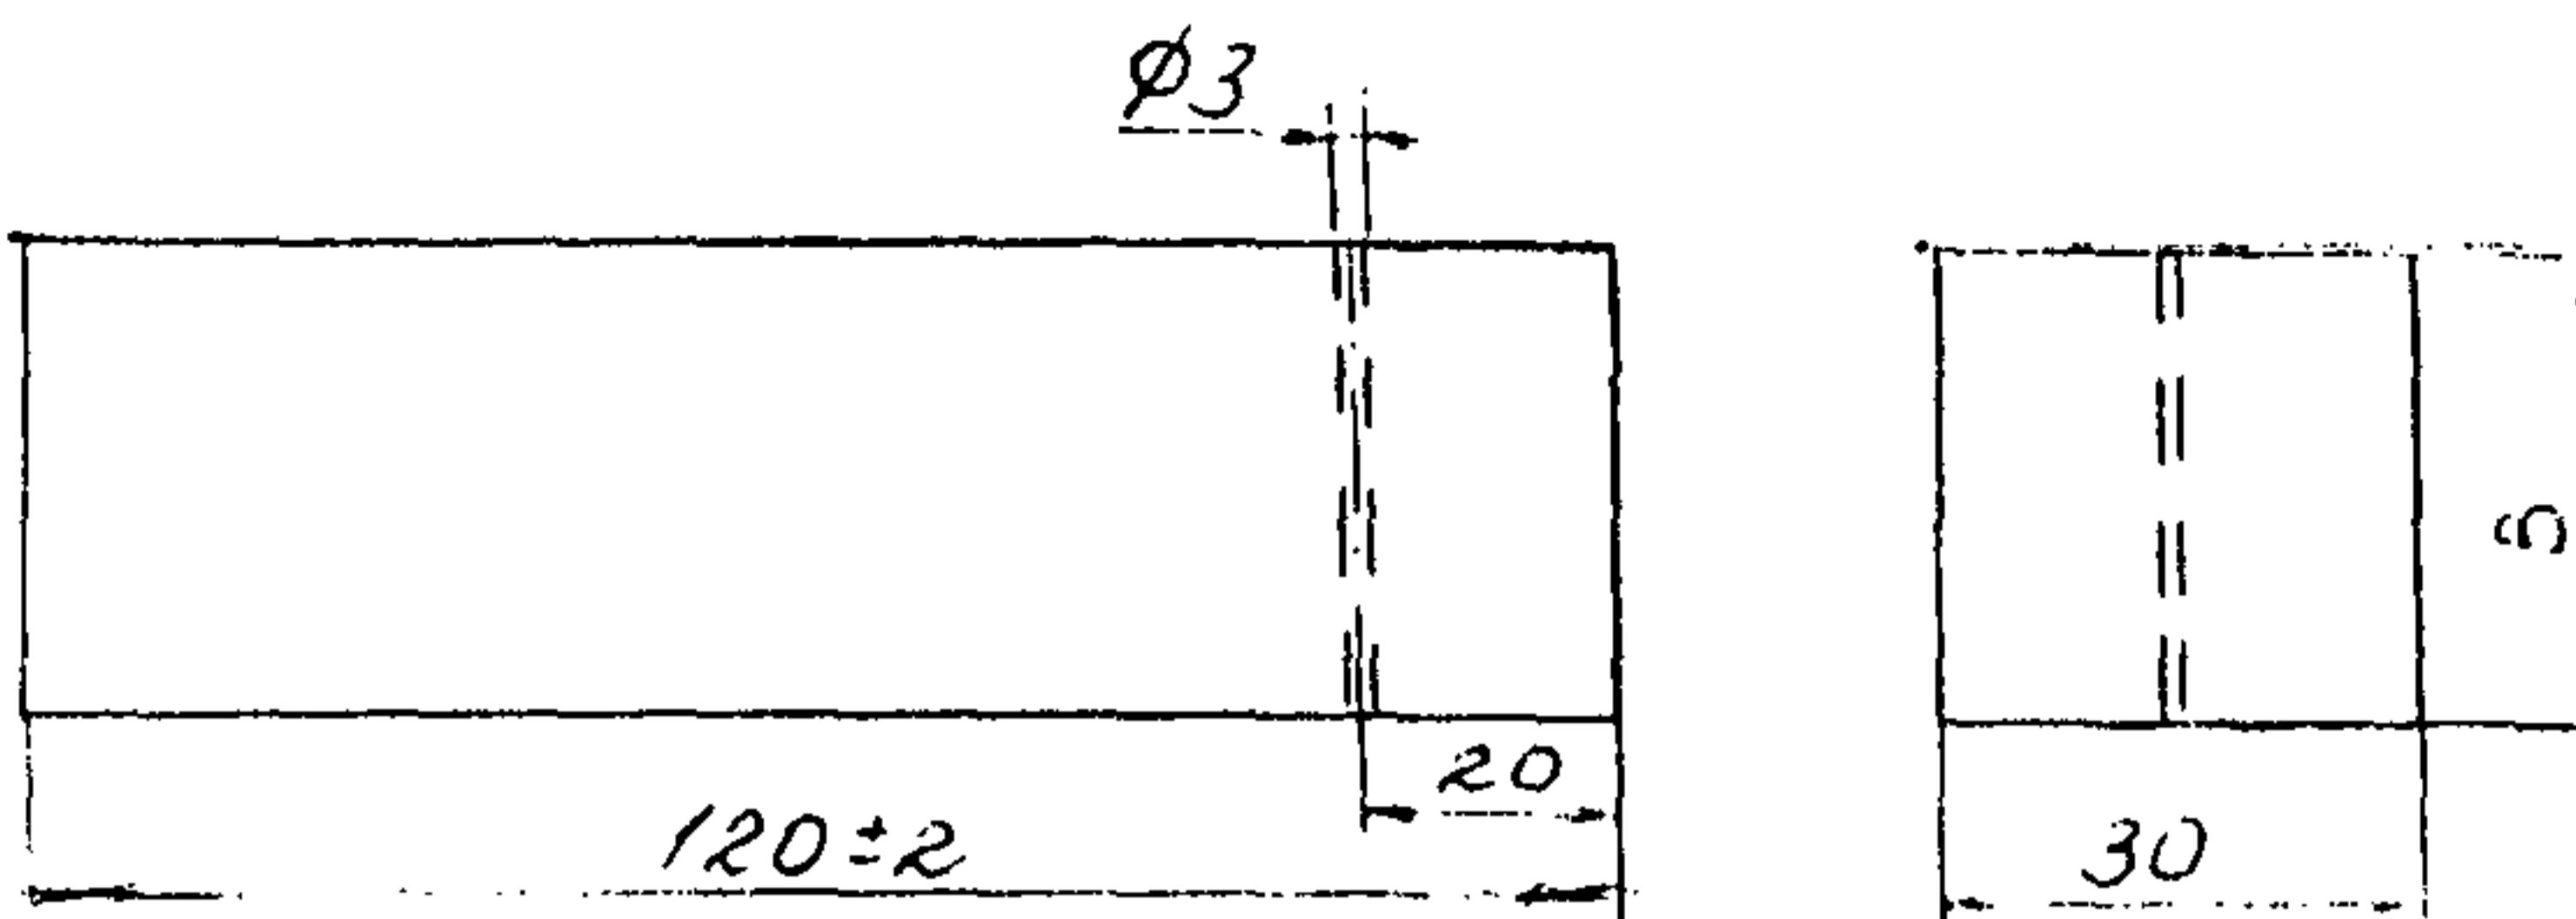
Стандартный образец предприятия и схема настройки скорости развертки и чувствительности УЗК Т-образного хвостового соединения обода диска ротора без разлопачивания
